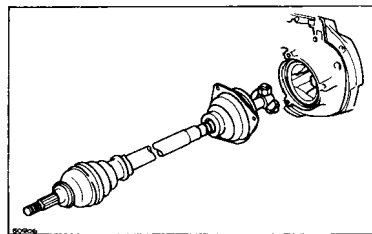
Вал привода левого колеса в сборе с шарнирами ШРУС
